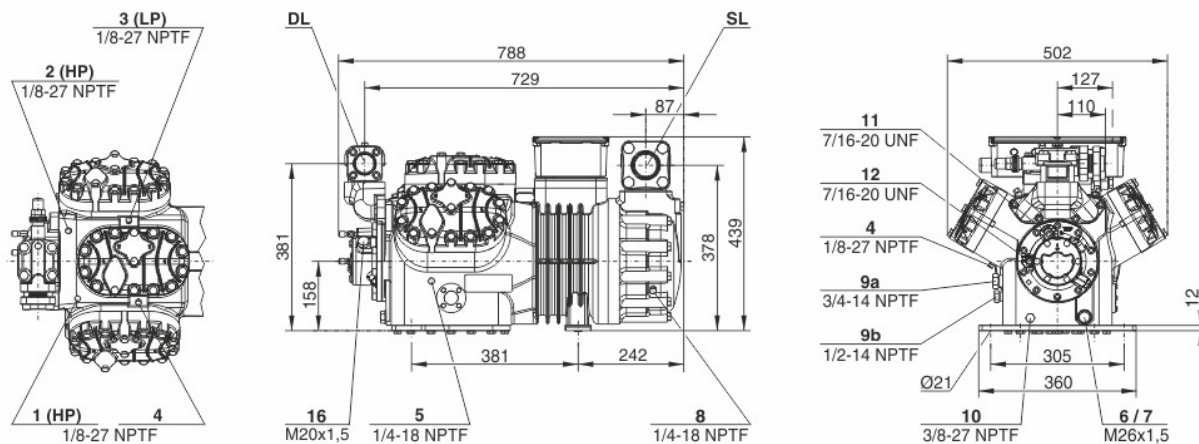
Компресорний агрегат Bitzer 6GE-40Y-40P.
